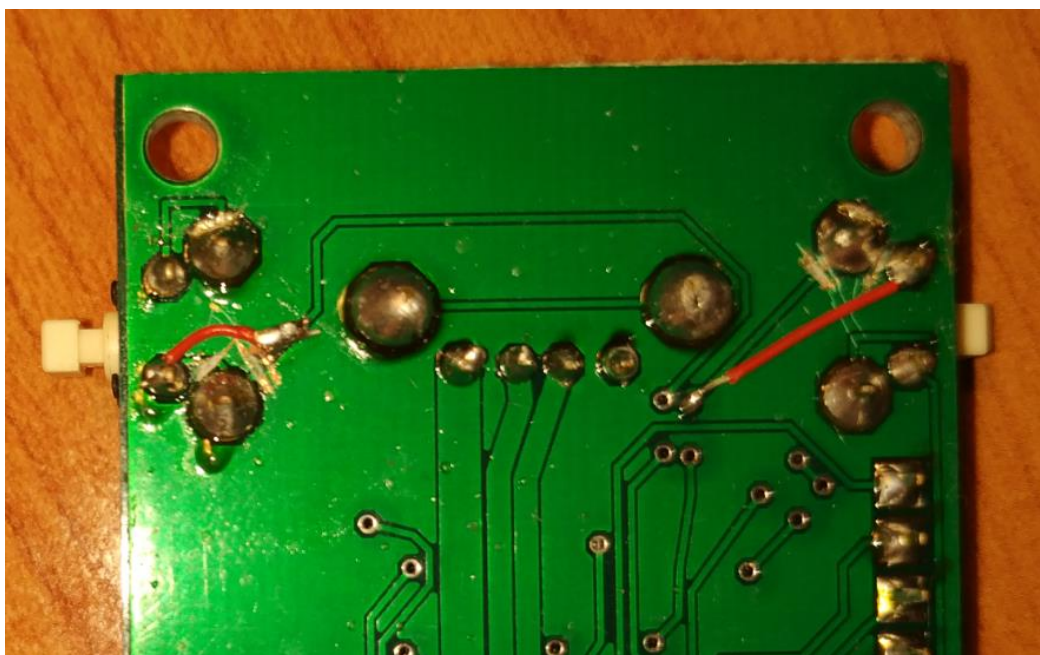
Modificación soldadura de los botones de la PCB
